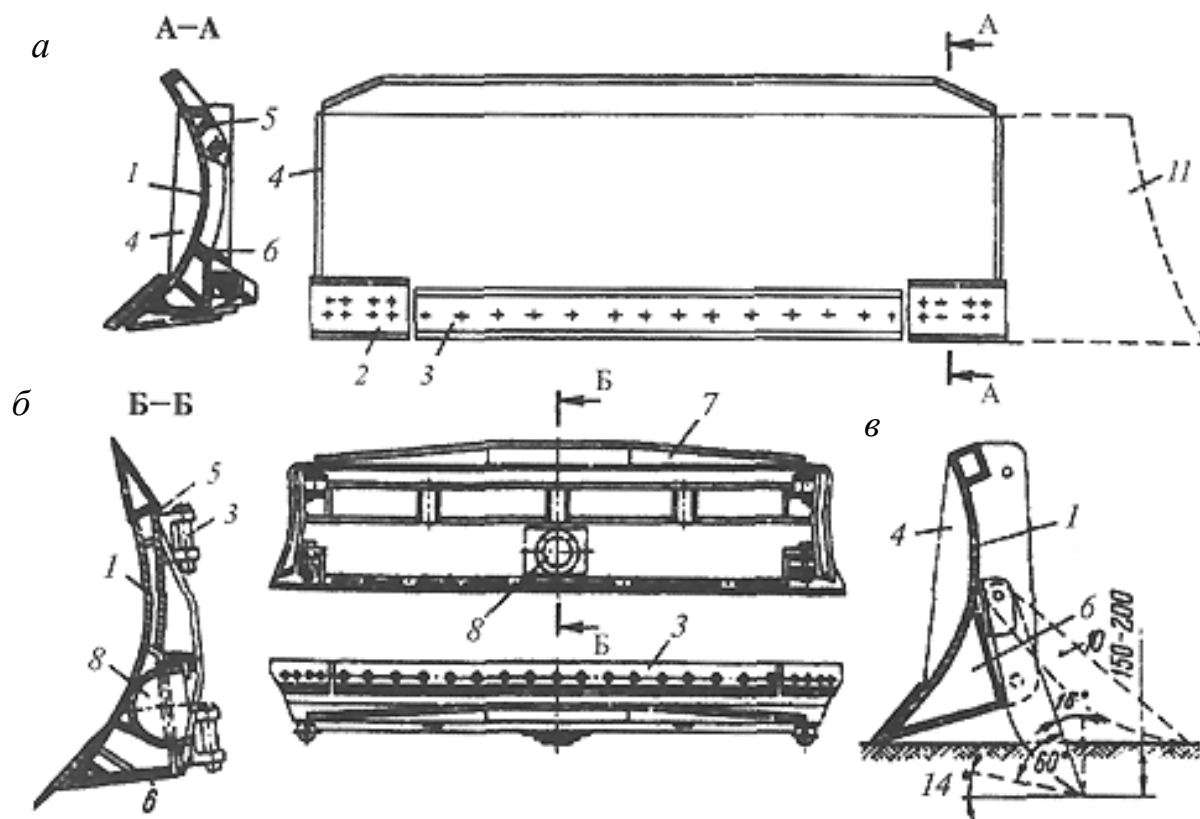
Конструкции бульдозерных отвалов: *а* – неповоротного; *б* – поворотного; *в* – со сменным рыхлящим зубом; 1 – лобовой лист; 2, 3 – ножи боковой и средней соответственно; 4 – боковина; 5, 6 – верхняя и нижняя коробки; 7 – козырек; 8 – подпятник для шарнирной головки; 9 – палец крепления отвала к боковым цапфам; 10 – зуб; 11 – открьлок-удлиннитель
